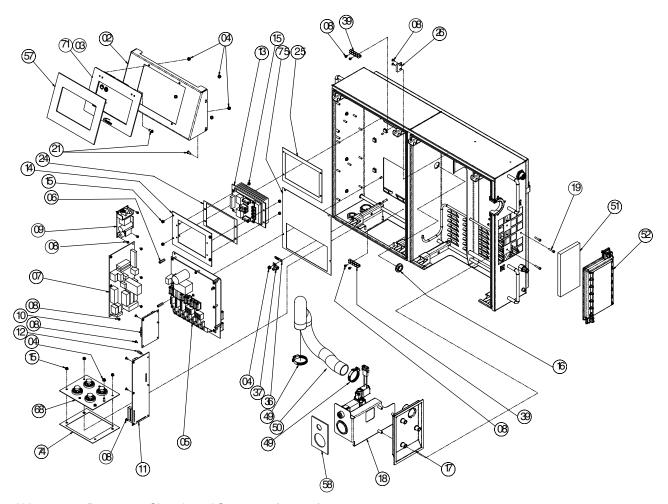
Baugruppe Chassis und Steuerung (2 von 3)
